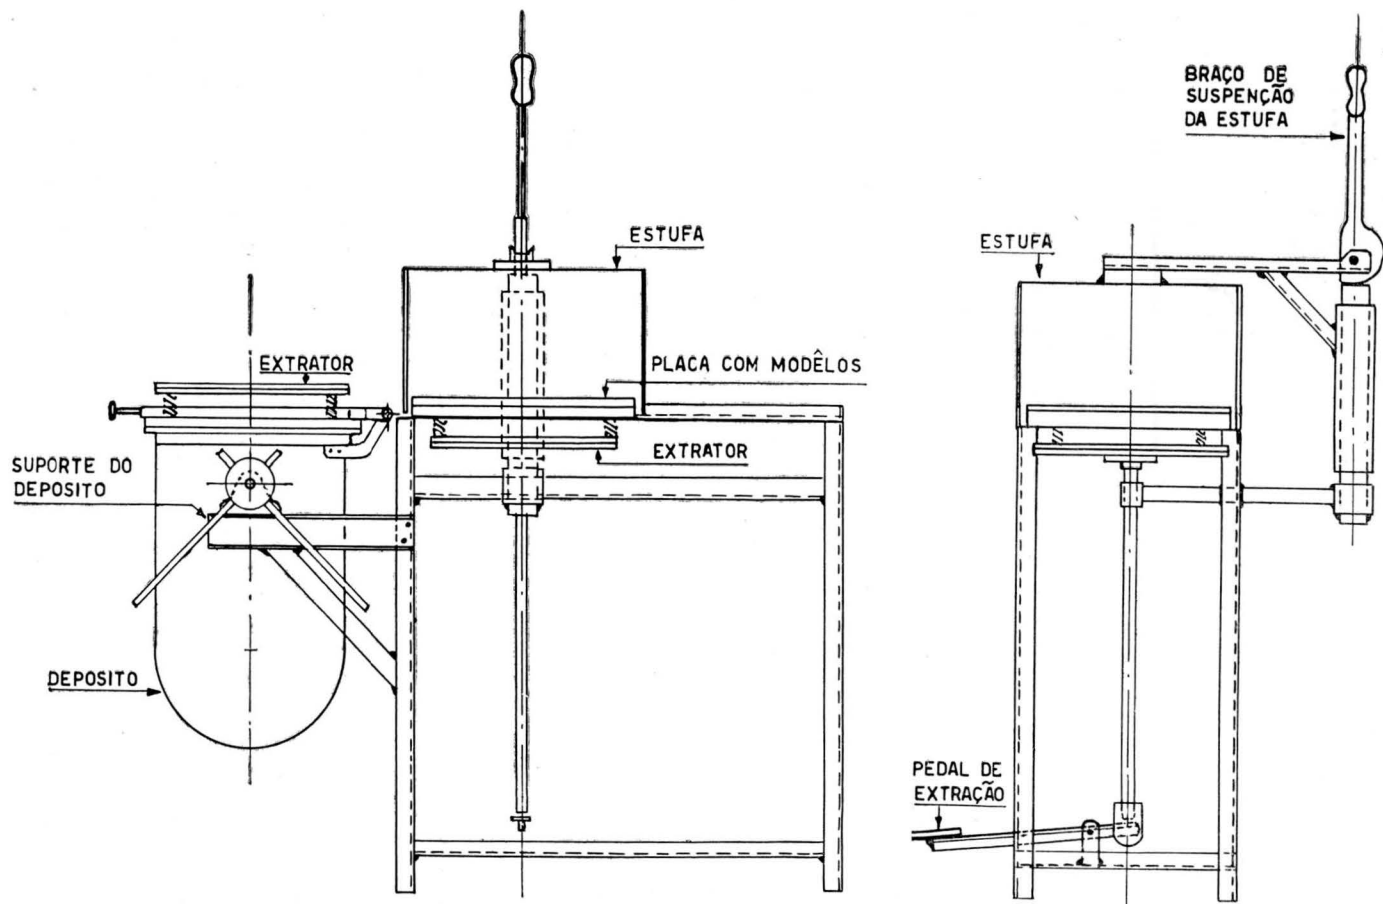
Esquema da máquina para moldagem em casca, projetada e construída no I.P.T.
